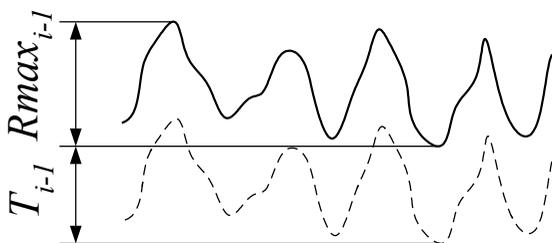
Схема поверхностного слоя материала поверхности заготовки
